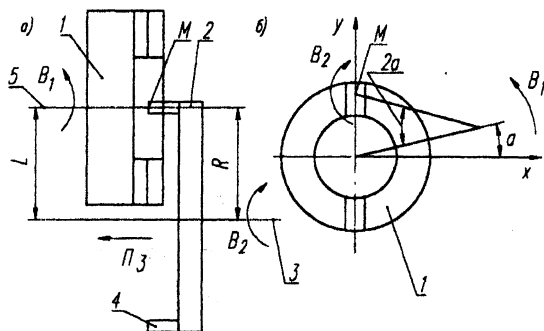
Схема обработки пазов торцевой резцовой головкой: а – кинематическая схема обработки, б – схема формообразования паза.
